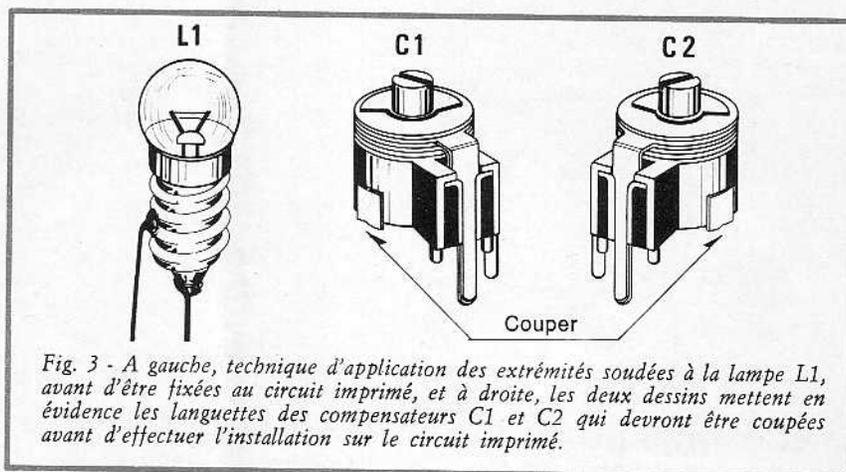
A gauche, technique d'application des extrémités soudées à la lampe L1, avant d'être fixées au circuit imprimé, et à droite, les deux dessins mettent en évidence les languettes des compensateurs C1 et C2 qui devront être coupées avant d'effectuer l'installation sur le circuit imprimé.
